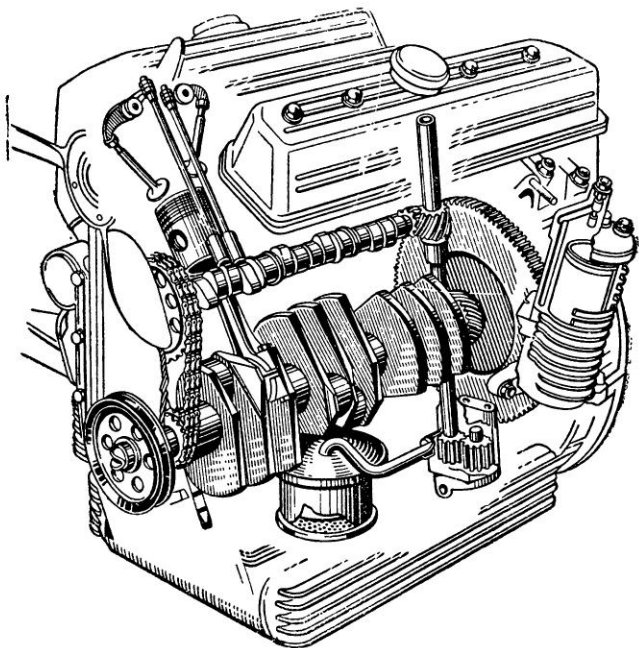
Привод верхнего распределительного вала бесшумной цепью
